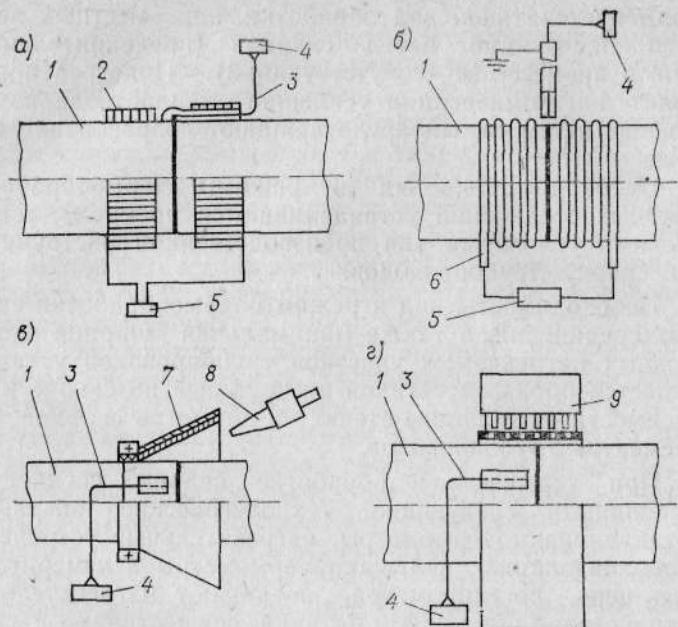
Нагревательные устройства для термической обработки сварных соединений
